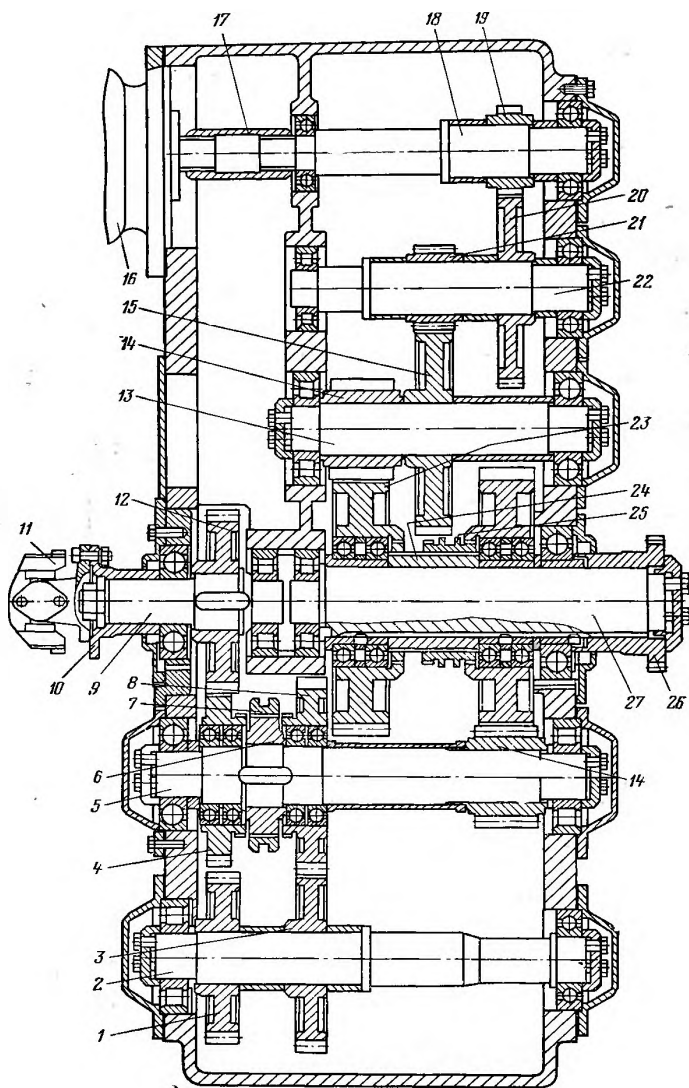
Редуктор хода экскаватора ЭТР253
